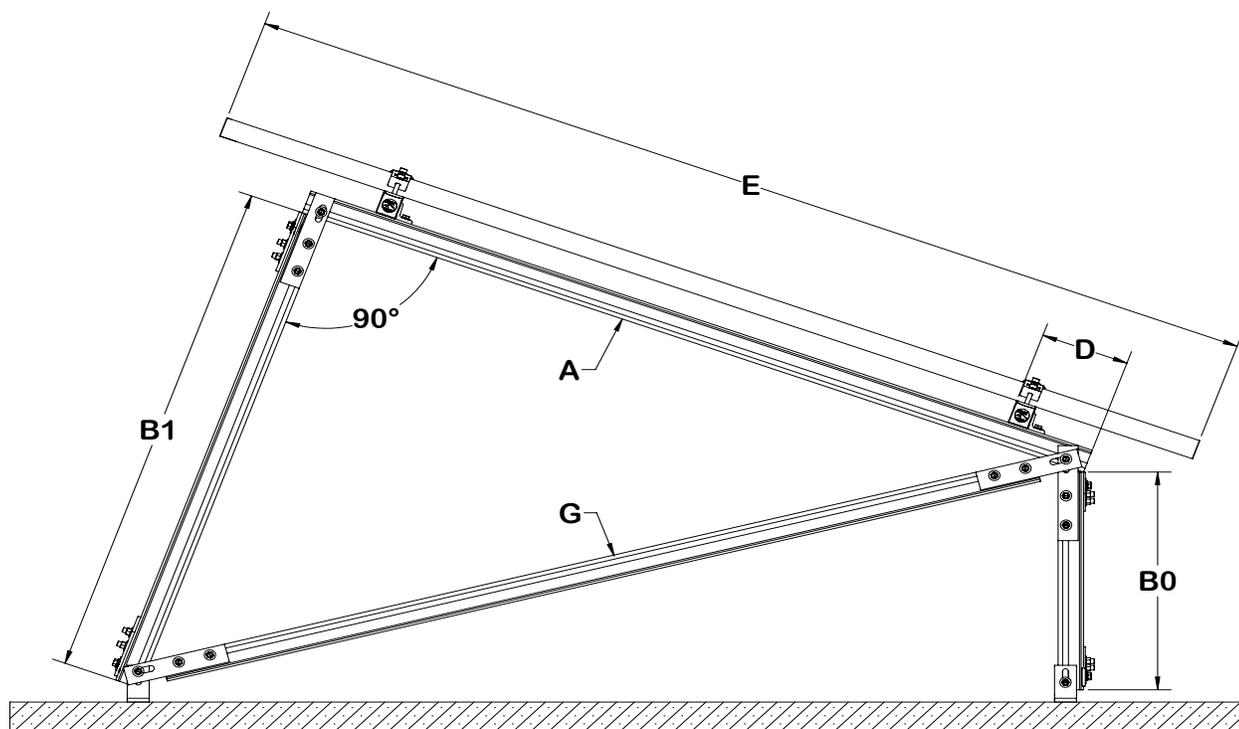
Dimensiones de ensamblaje para el sistema Tilt Up Single-Raised de 1 Fila.
